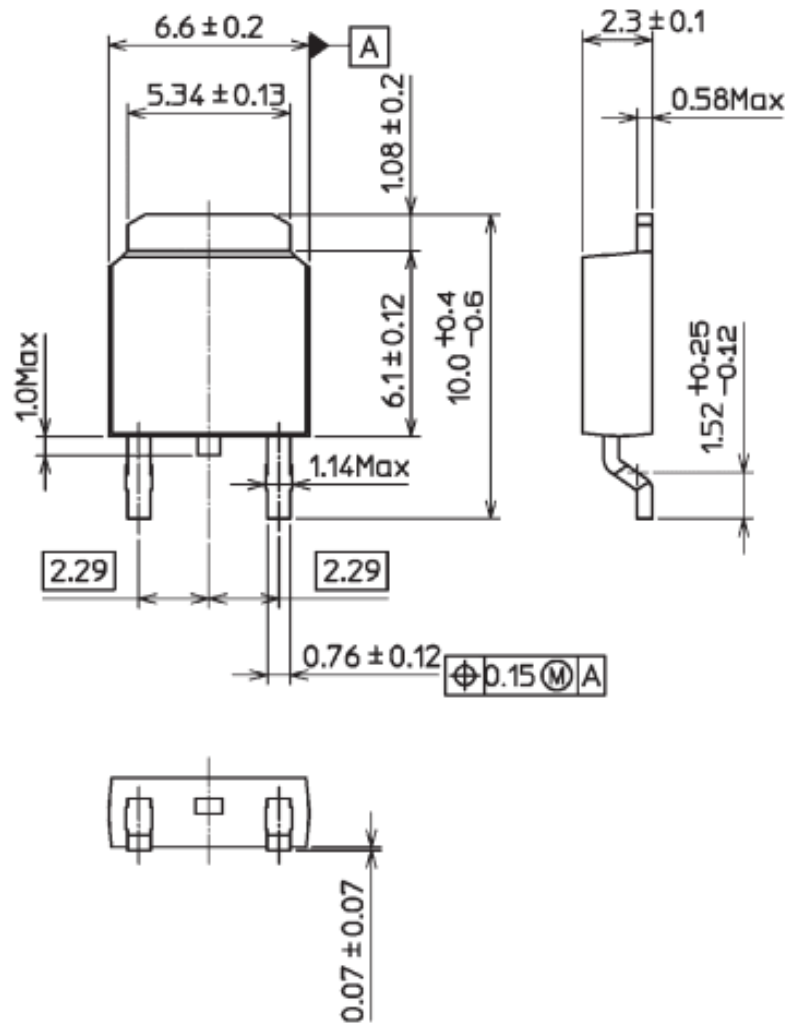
Розміри стабілізатора напруги в корпусі TO-263
